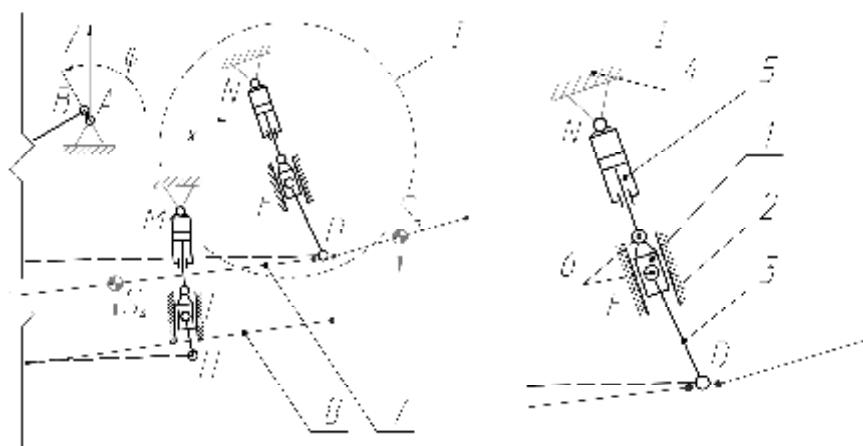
Кинематическая схема усовершенствованного механизма привода очистки с автоматическим продольным выравниванием решет: 1 – ползун; 2 – направляющая; 3 – подвеска решета; 4 – рама комбайна; 5 – управляющий гидроцилиндр; 6 – поворотный шарнир; 7 – верхнее решето; 8 – нижнее решето
